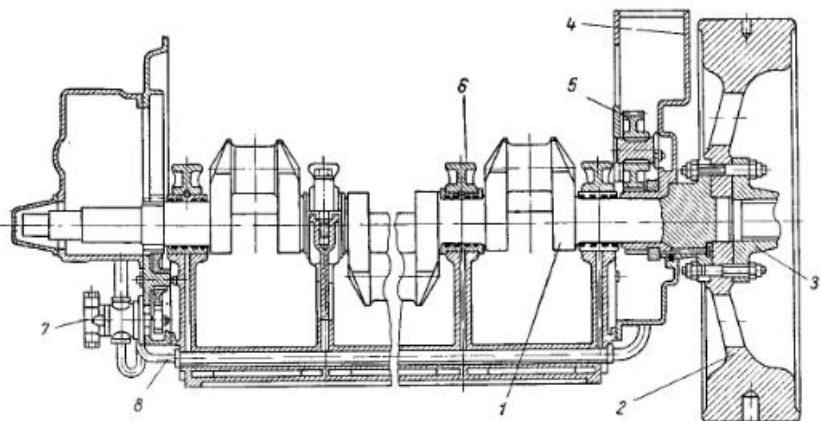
Коленчатый вал двигателей типа NVD-24:
